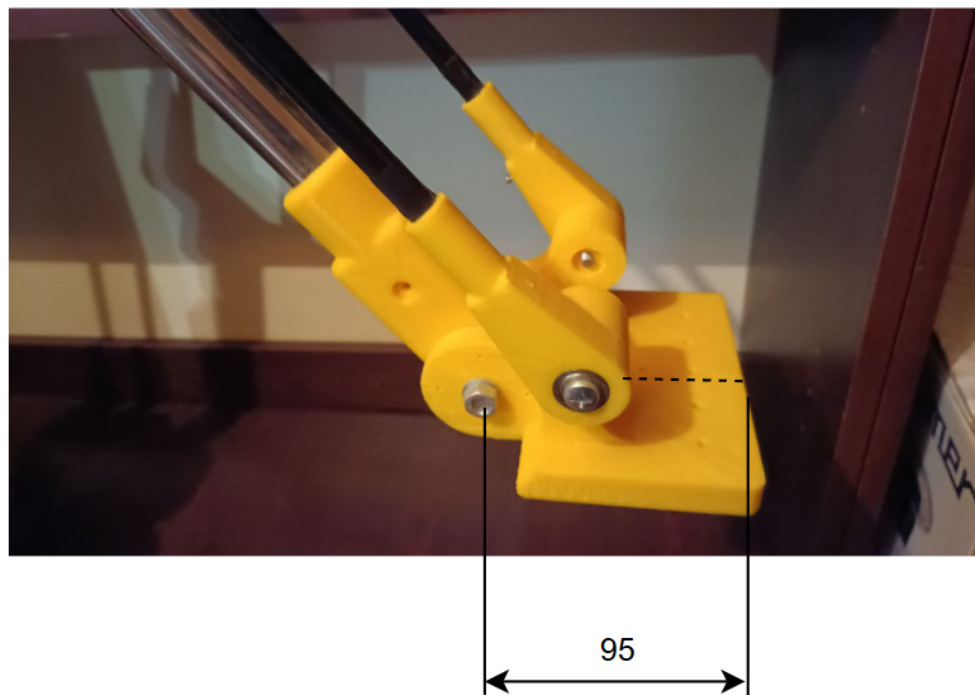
Конструкція платформи для кріплення інструменту
